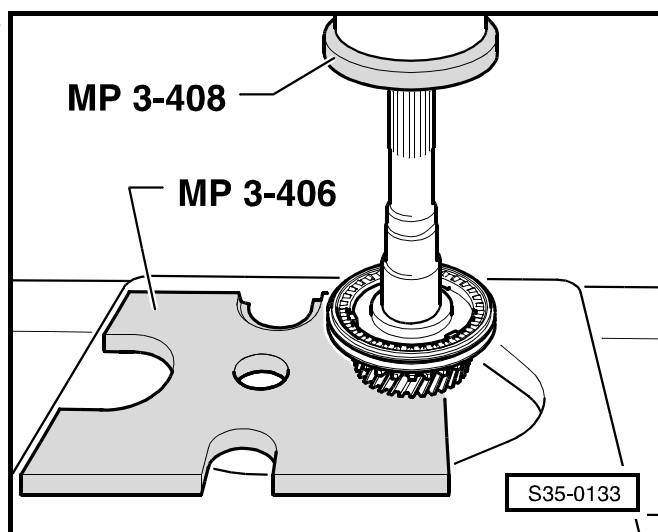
Разборка и сборка скользящей муфты и каретки синхронизатора 3-ей и 4-ой передач ►
